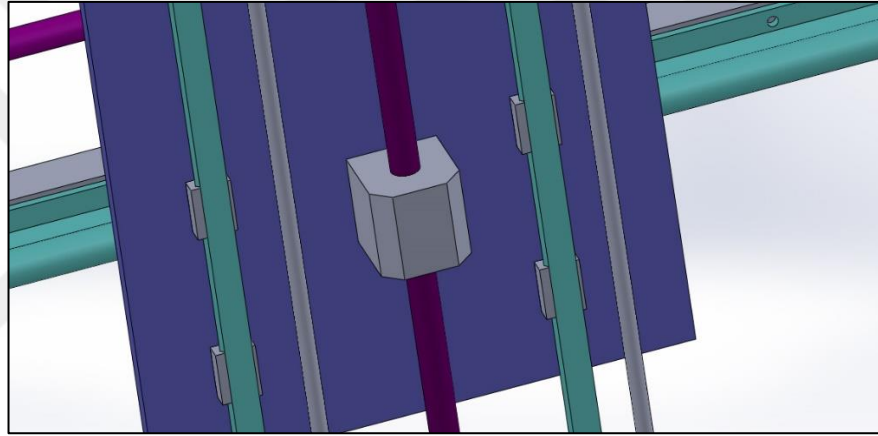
Z eksen motor ve vidalı mil şasesi montajı (alt kısım)
